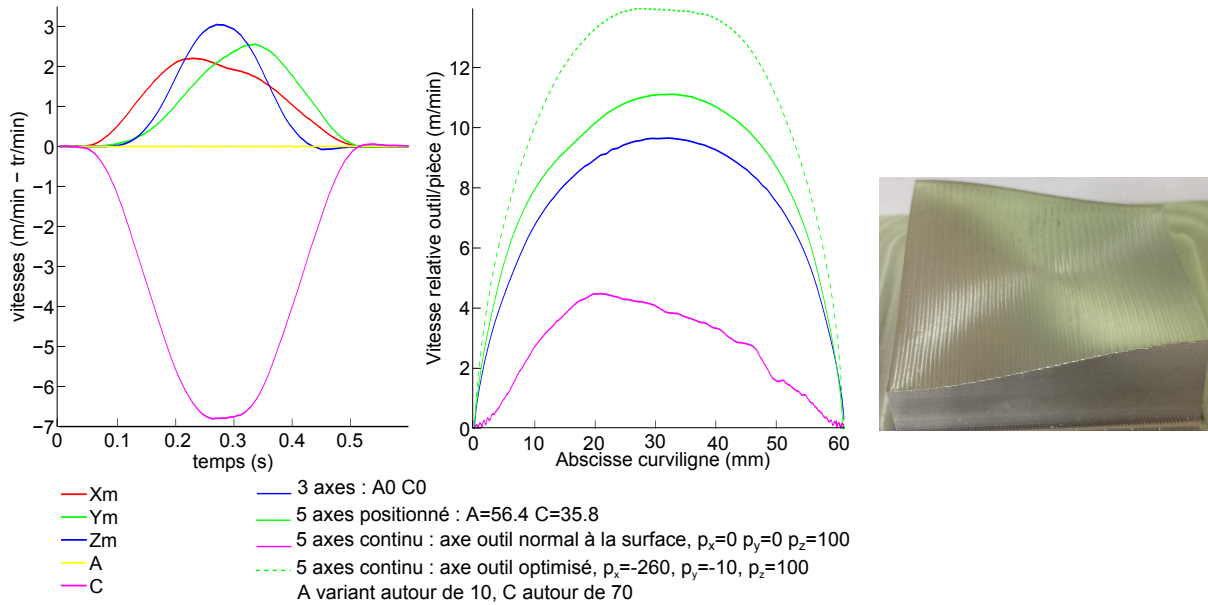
Mesures cinématiques et pièce usinée
